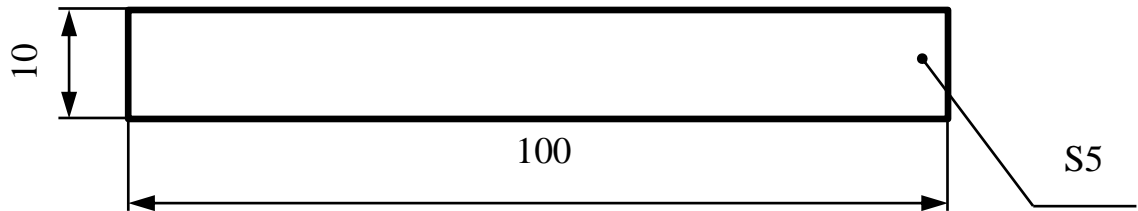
Ескіз заготовки для виготовлення зразків.
